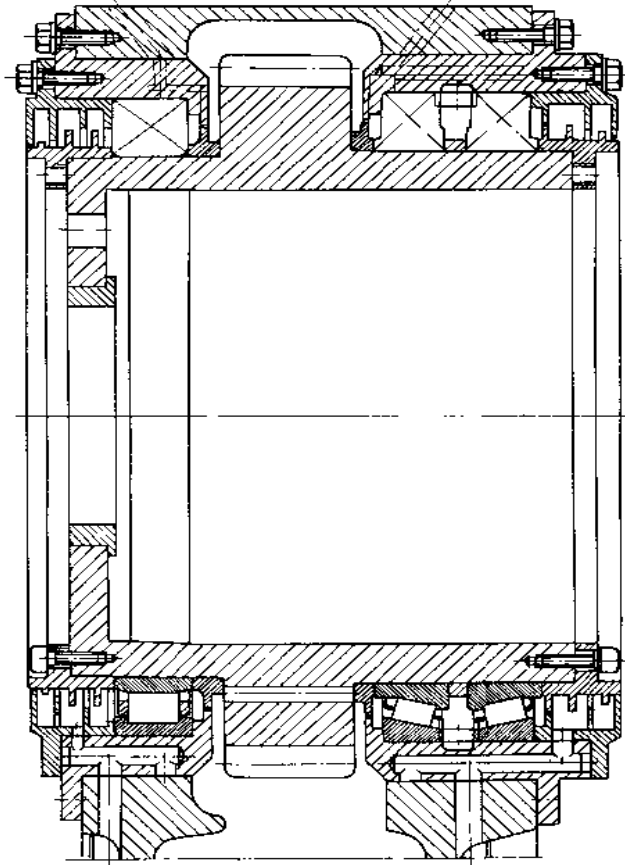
高速火车减速器输出端行星齿轮轴支承
